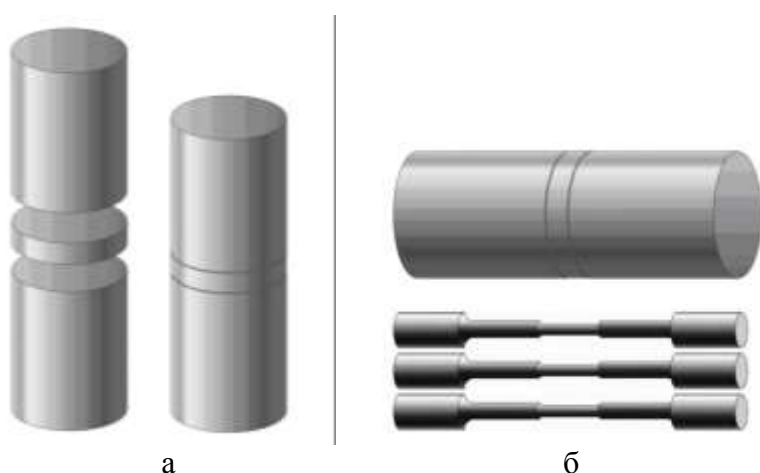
Схема сварки давлением образцов через прослойку (а) и вырезки после сварки (б)
